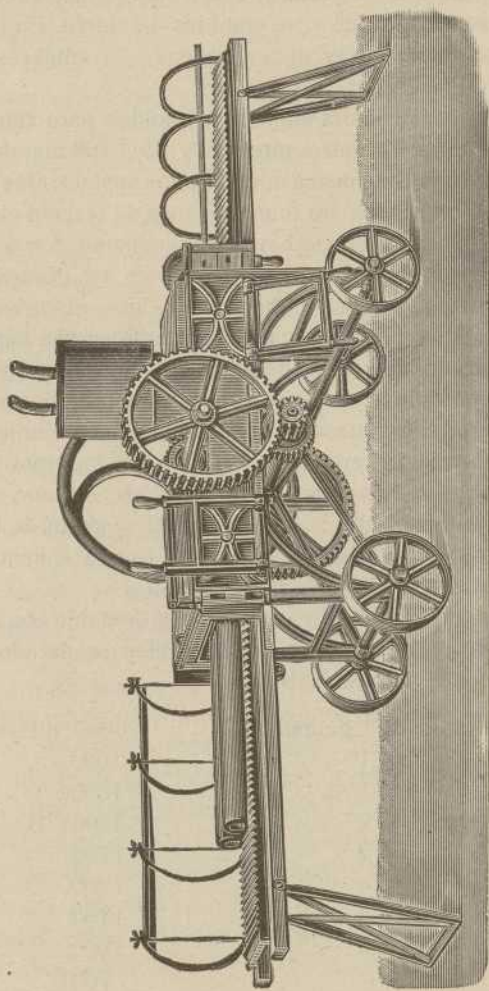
Prensa de doble efecto para fabricar tubos.
